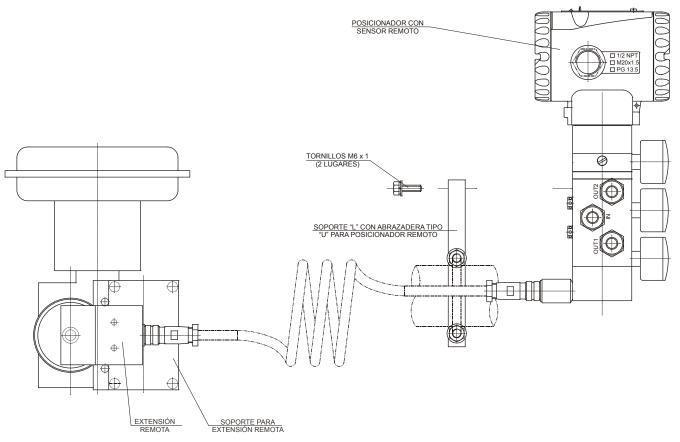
Posicionador en Actuador Rotativo con Sensor de Posición Remoto
